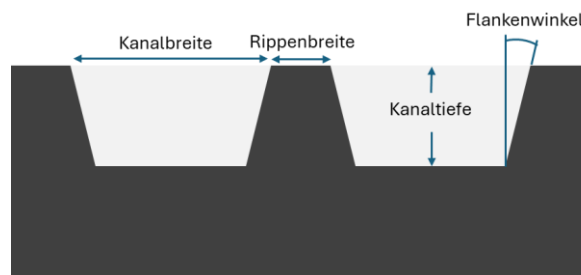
Geometrieüberlegungen für die Auslegung von Prägwerkzeugen auf Basis des Kanalquerschnitts
